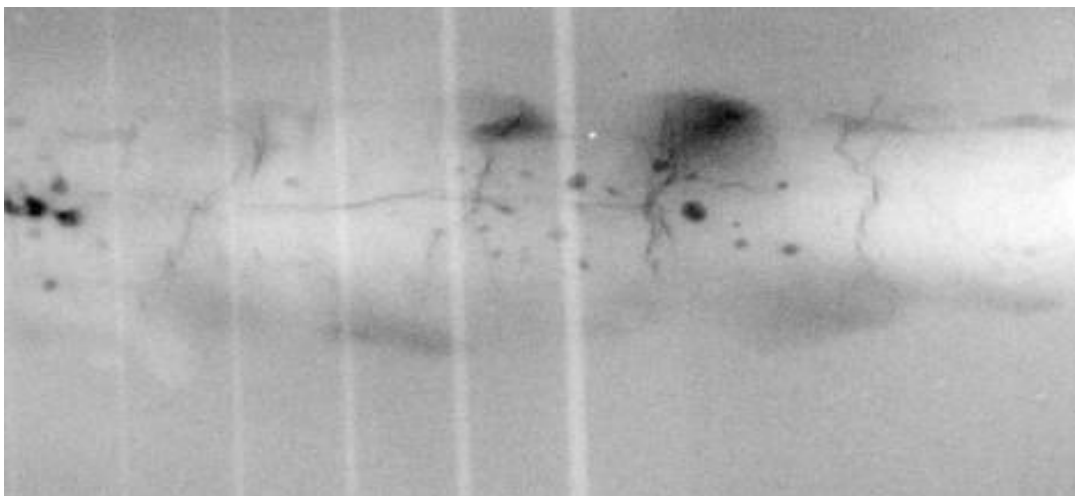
Radiografía soldadura de Acero al Carbono por la técnica convencional (RTC).
